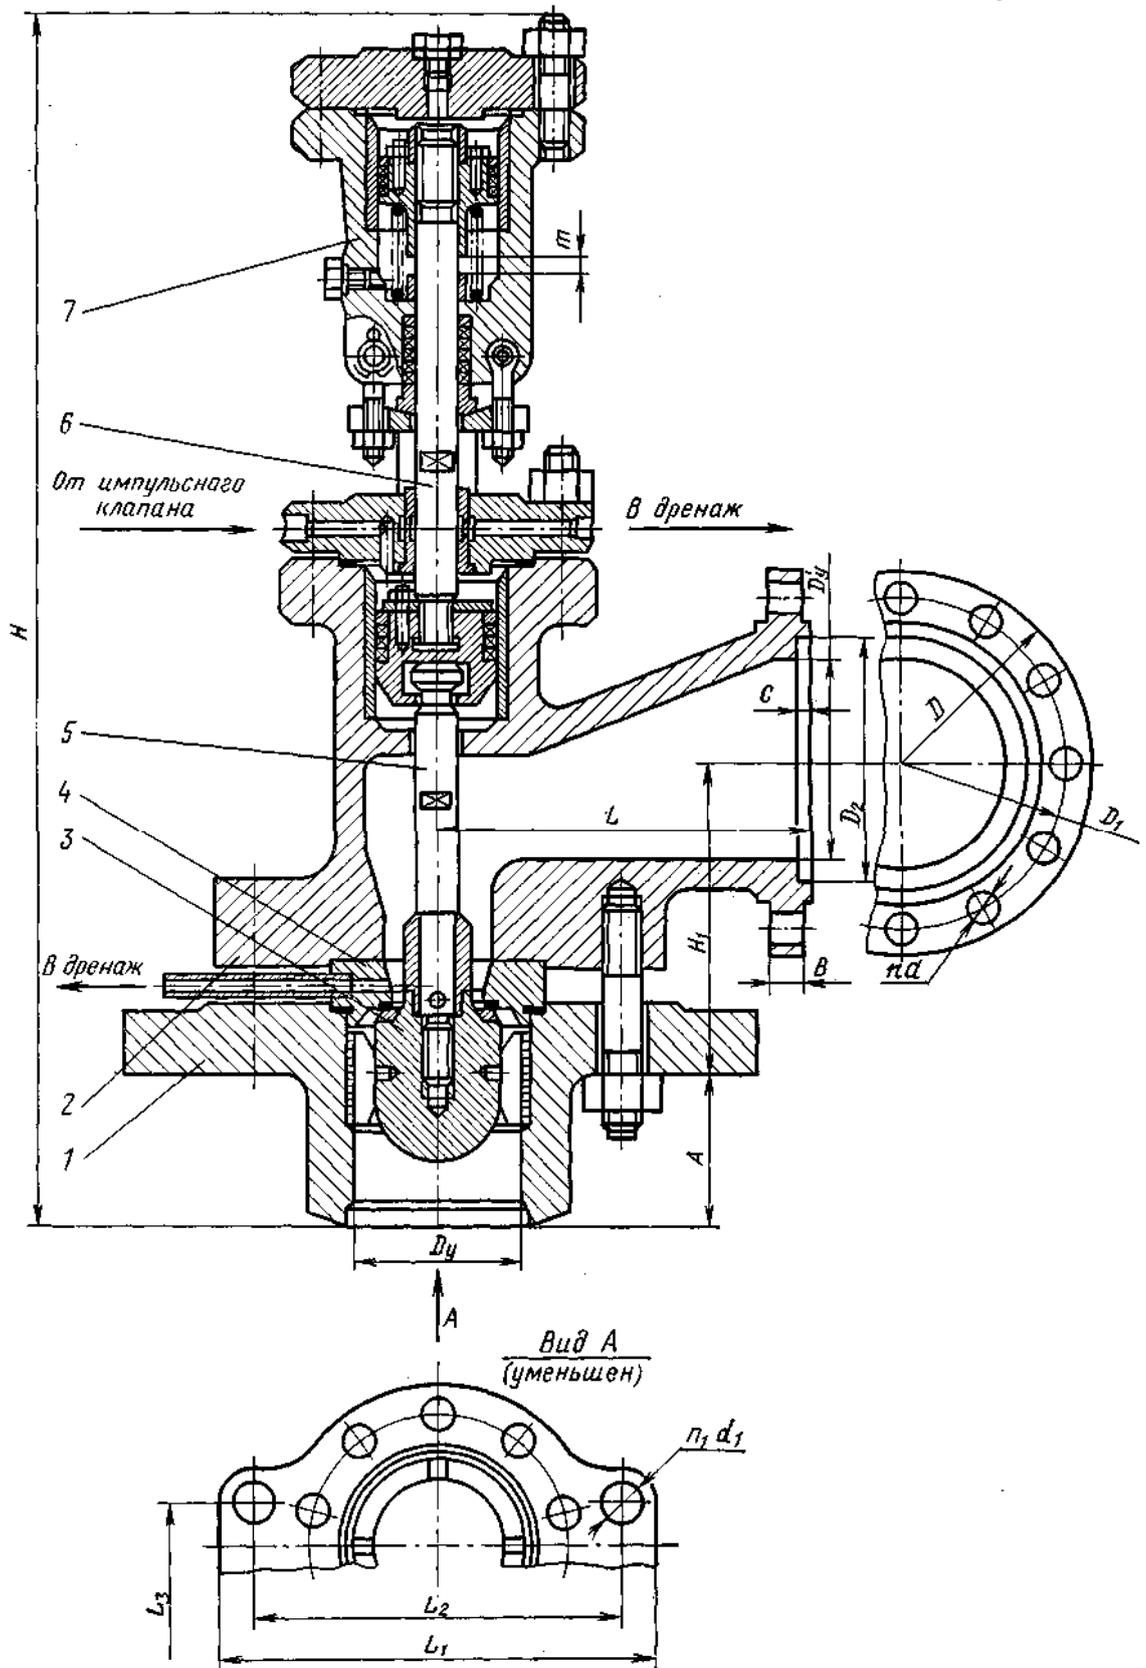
Главный предохранительный клапан серий 875 и 392.
